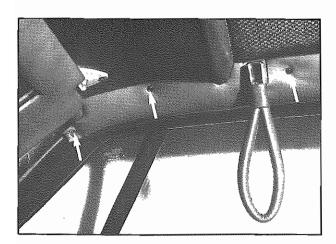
Viti di fissaggio rivestimenti Coverings screws
